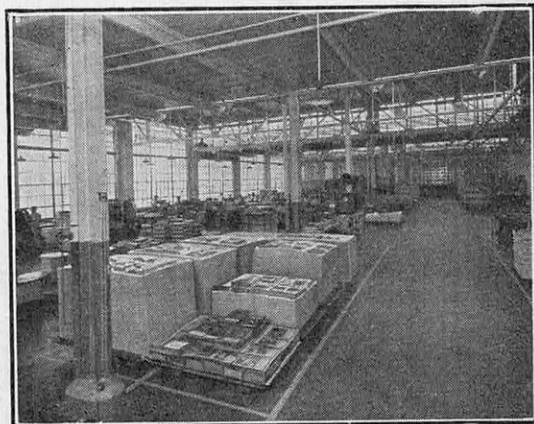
Après impression, le papier passe aux ateliers de finition et de façonnage.
